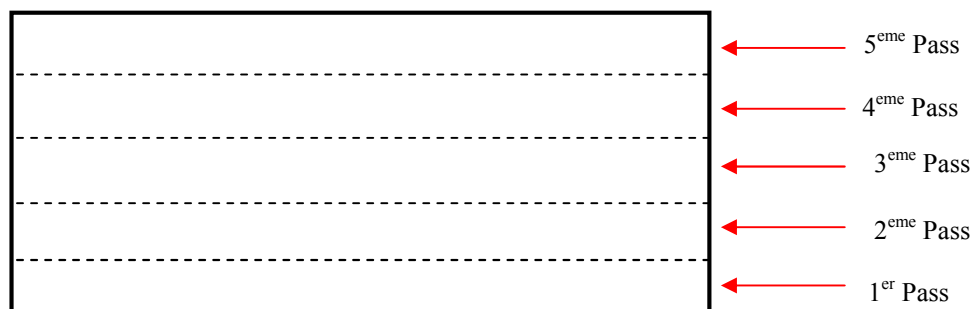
Première stratégie de génération des passes sur la surface usinée.
